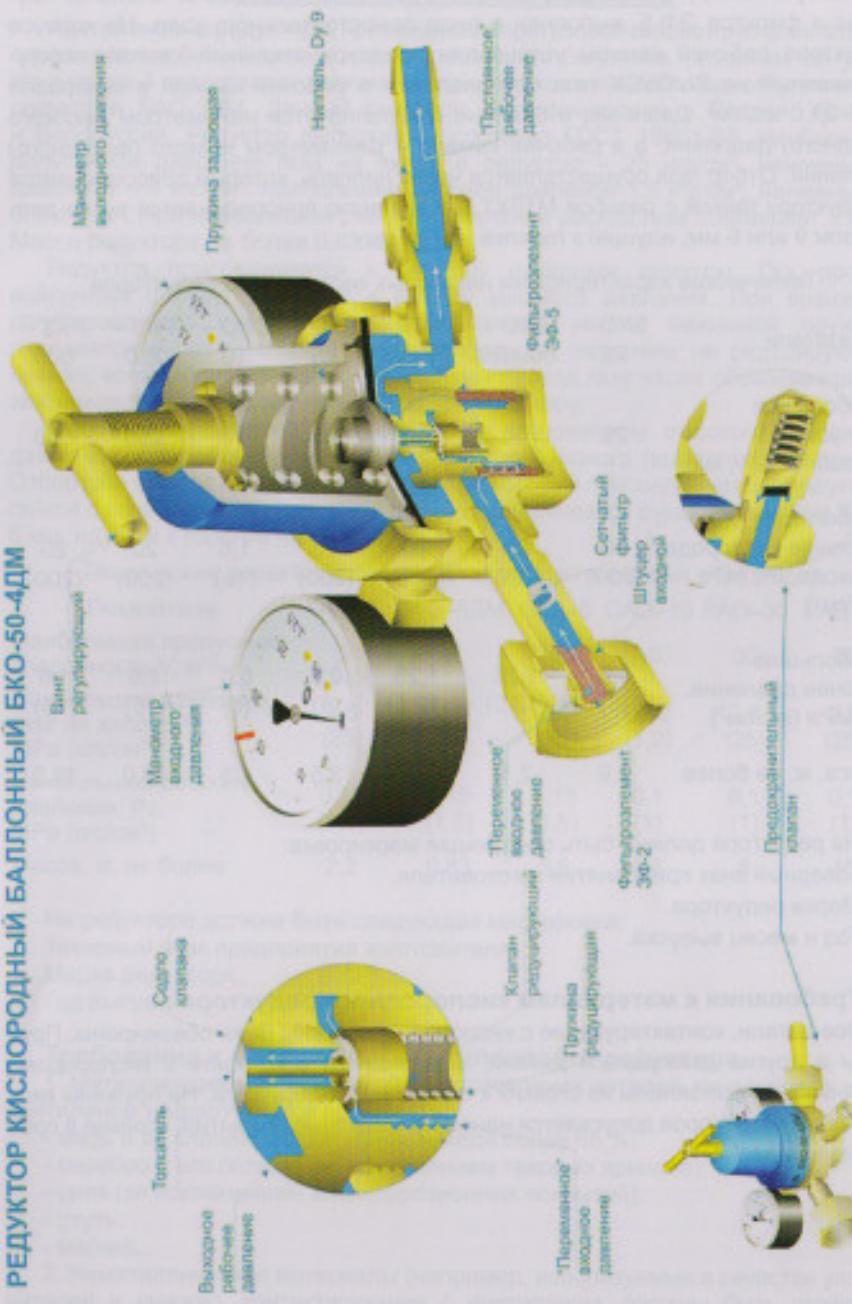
Схема кислородного редуктора БКО-50-4ДМ
